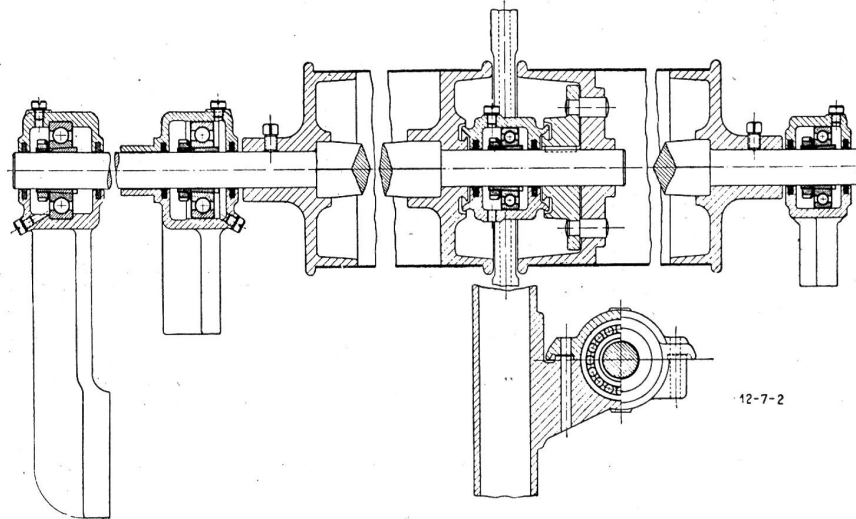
Kugellagerung in einer Schlichtmaschine.
